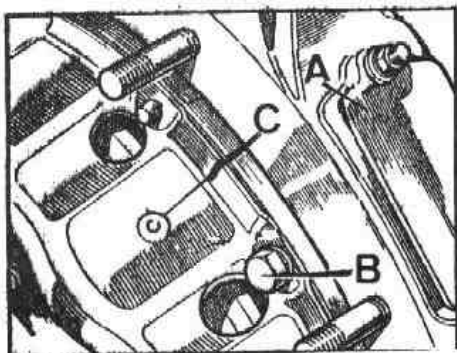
Desmontaje del plato de presión y disco de embrague
